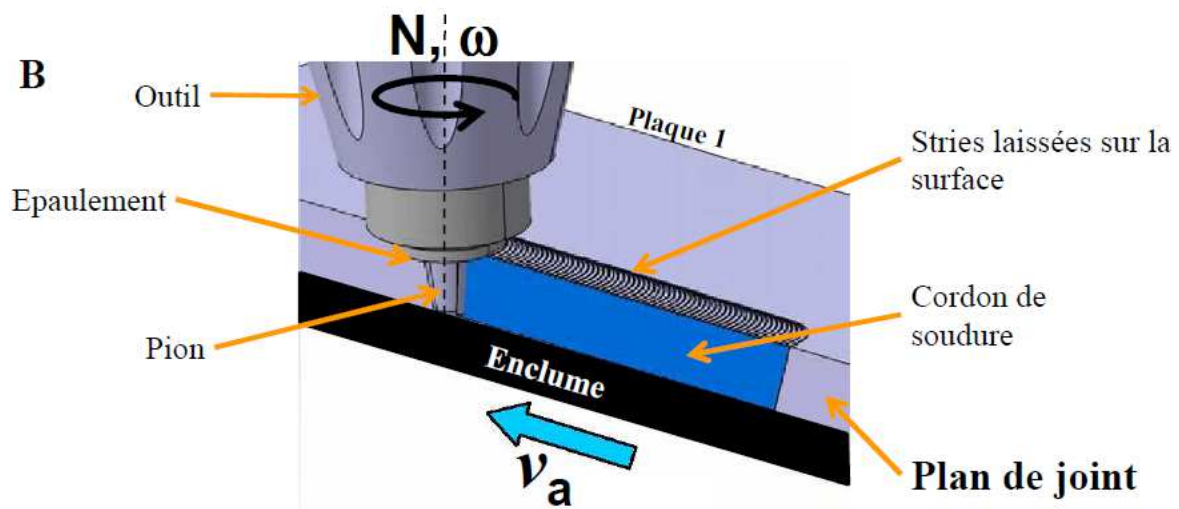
Présentation du soudage par friction-malaxage.[3].
